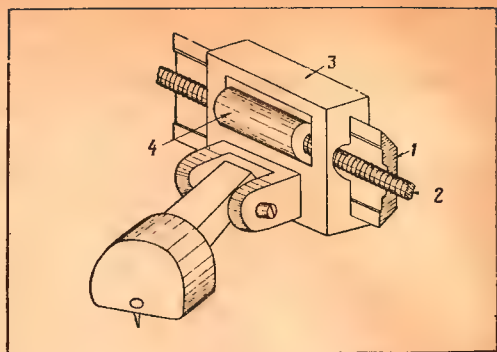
Направляющая в виде «ласточкин-го хвоста». 1 — неподвижная рейка; 2 — ходовой винт, 3 — ползун; 4 — ведущая гайка
